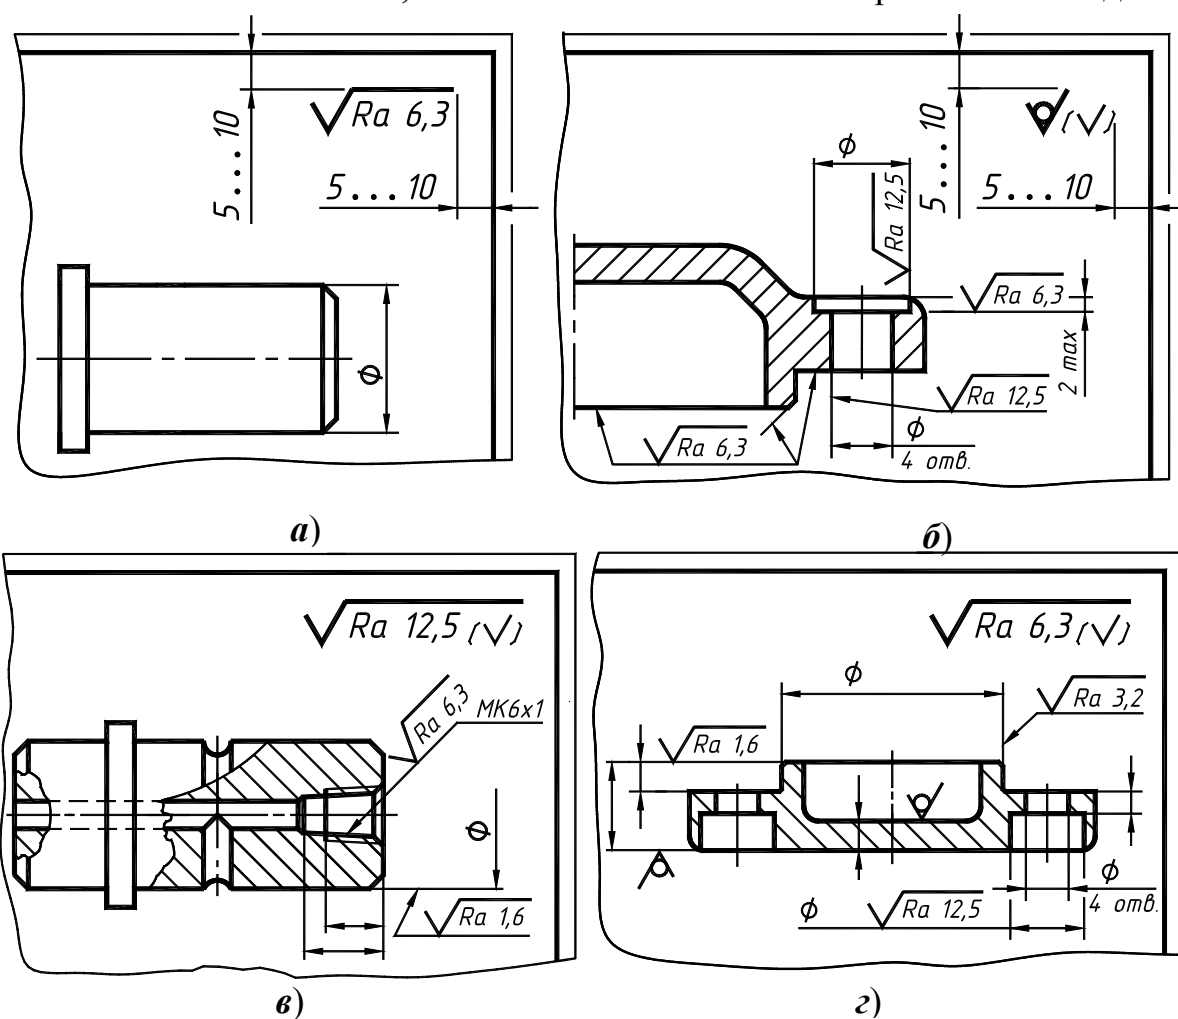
Примеры простановки знаков шероховатости поверхностей
